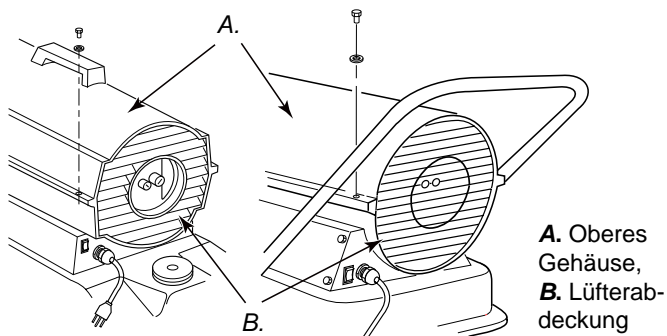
Entfernen des oberen Ge-häuses.
